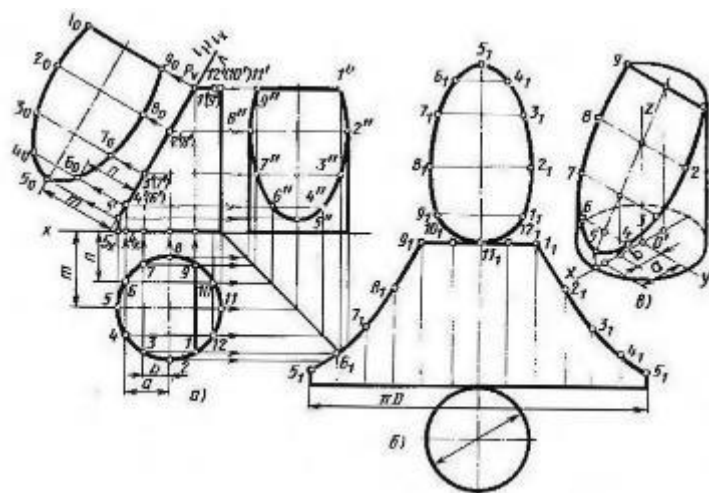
Комплексный чертеж, изометрия и развертка цилиндра
